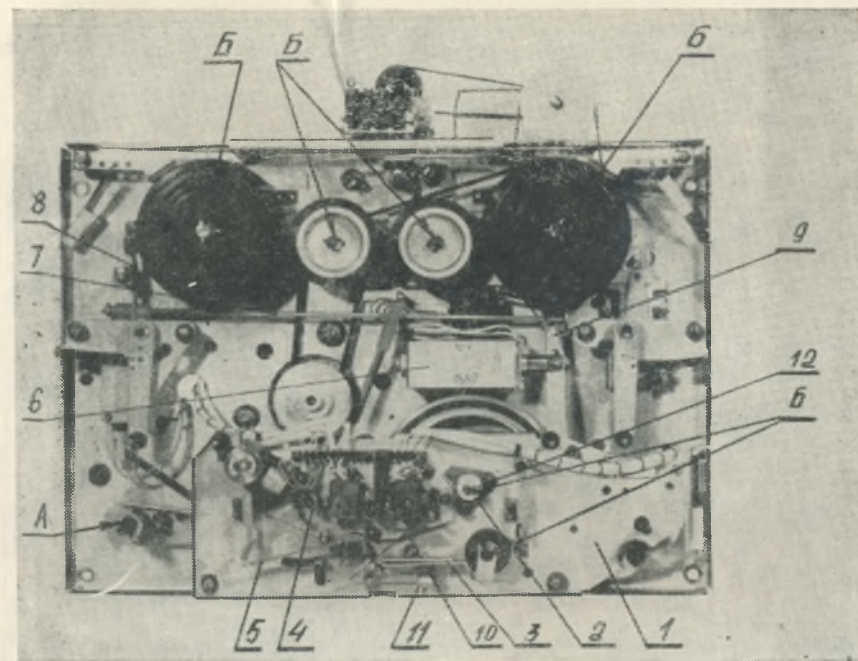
Лентопротяжный механизм. (Вид сверху):
